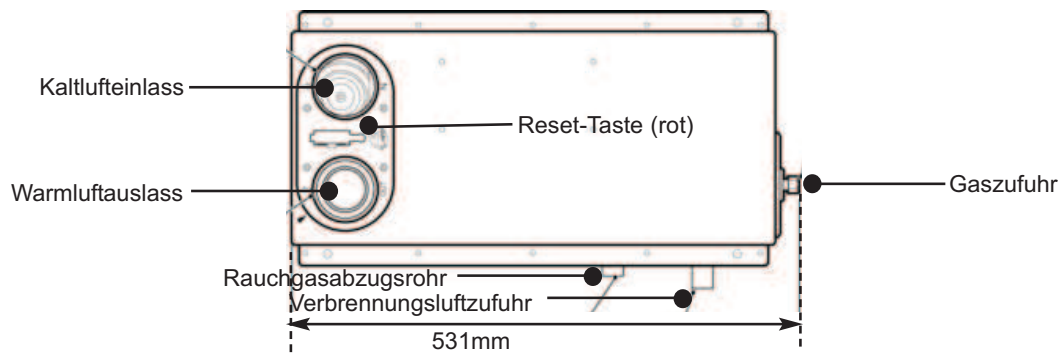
Unterbodenmontage - Draufsicht - SH2211 oder SC2211
